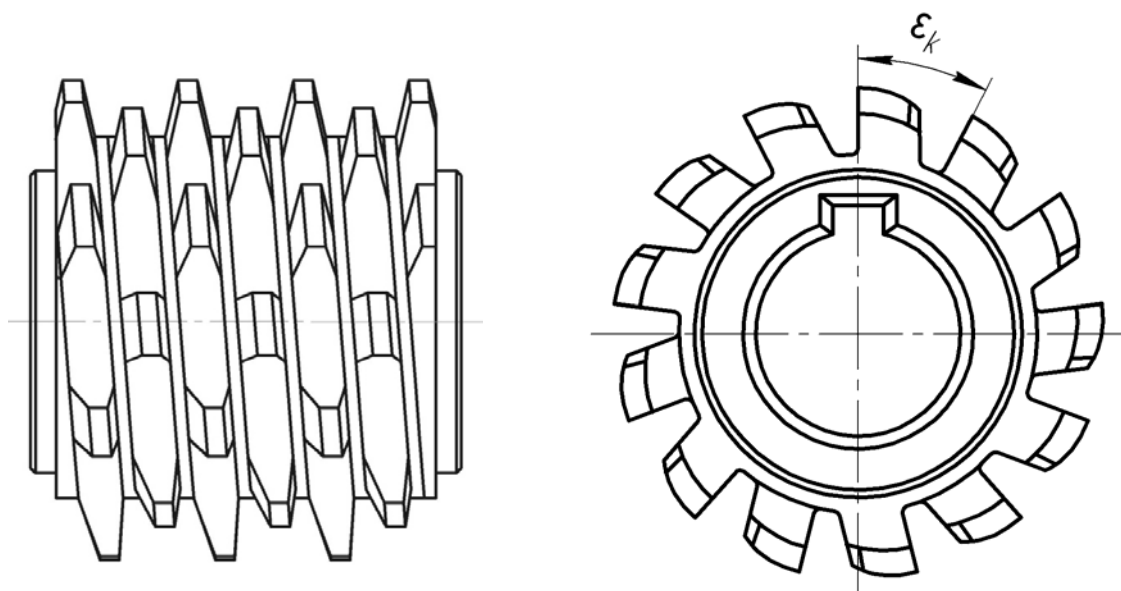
Червячная однозаходная фреза с шахматным расположением зубьев
